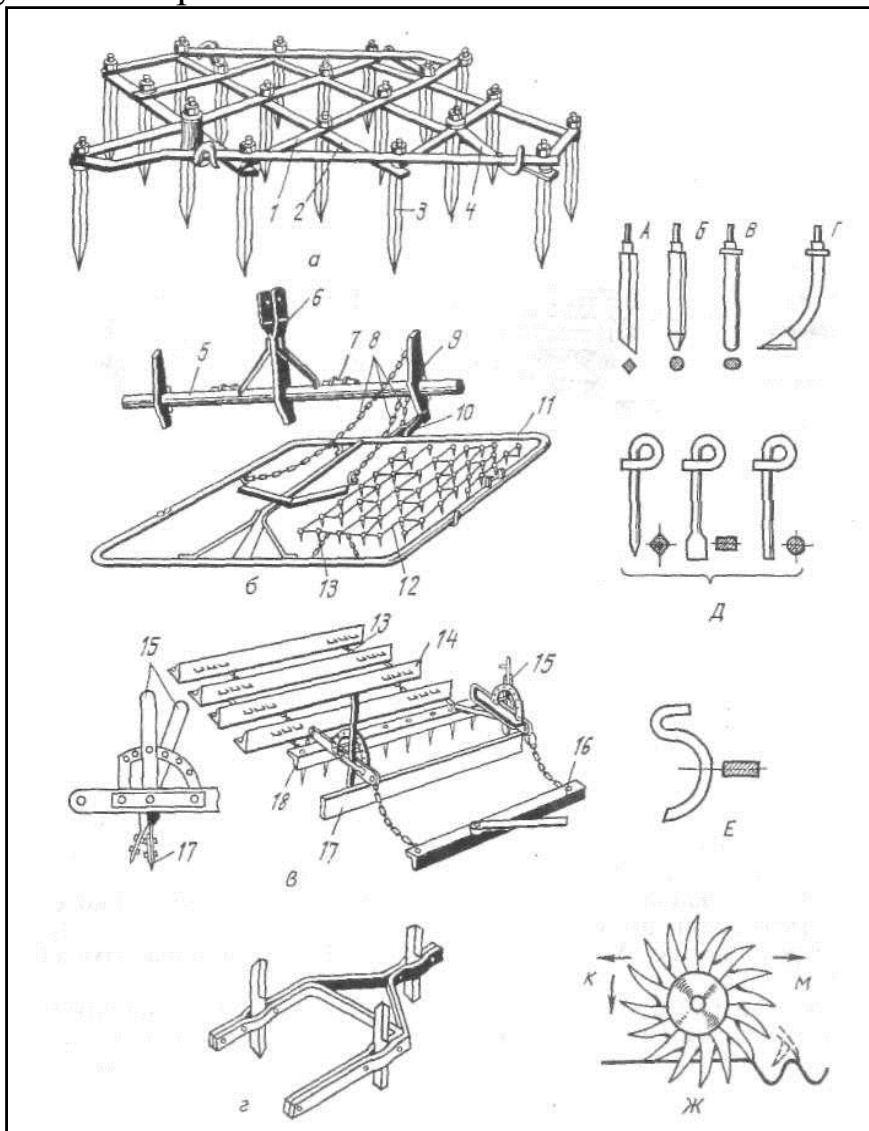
Бороны и их рабочие органы: а – зубовая БЗТС-1; б – сетчатая БСО-4; в – шлейф-борона ШБ-2,5; г – звено луговой бороны с ножевидными зубьями; А – зуб квадратного сечения; Б – зуб круглого сечения; В – зуб овального сечения; Г – лапчатый зуб; Д – зубья сетчатой бороны; Е – зуб пружинной бороны; Ж – игольчатый диск мотыги; 1, 2, – планки рамы; 3 – зуб; 4 – прицепное устройство; 5 – брус навески; 6 – стойка; 7 – палец; 8, 13 – цепи; 9 – кронштейн; 10 – тяга; 11 – рамка; 12 – сетчатое полотно; 14 – шлейф; 15 – рычаг; 16 – вага; 17 – нож; 18 – грабли
